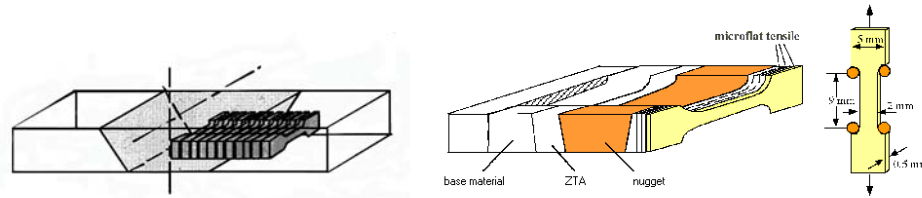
Esquema, em perspectiva, mostrando a retirada dos micro corpos de prova de um bloco contendo a junta soldada e as zonas resultantes da solda.
